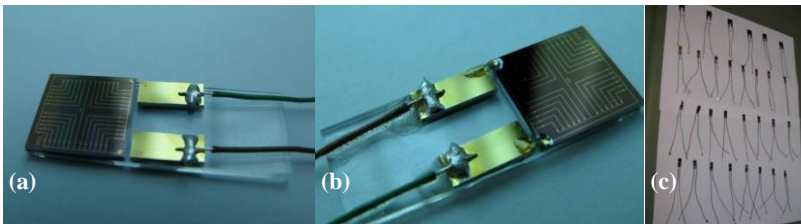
(a) dispositivo com os fios elétricos soldados; (b) pontos de cola epóxi sobre as soldagens e entre eletrodo e chip; e (c) dispositivos finalizados prontos para receber os nanotubos.
